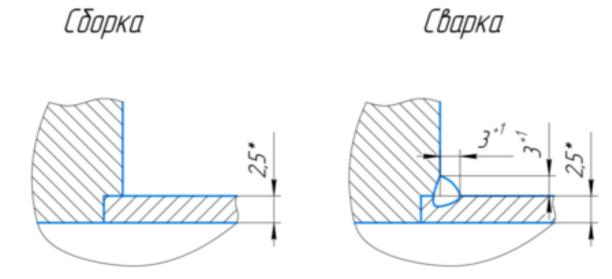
Общий вид шва, соединяющего фланец и патрубок (поз. 4) Режимы сварки шва приведены в таблице 3.
